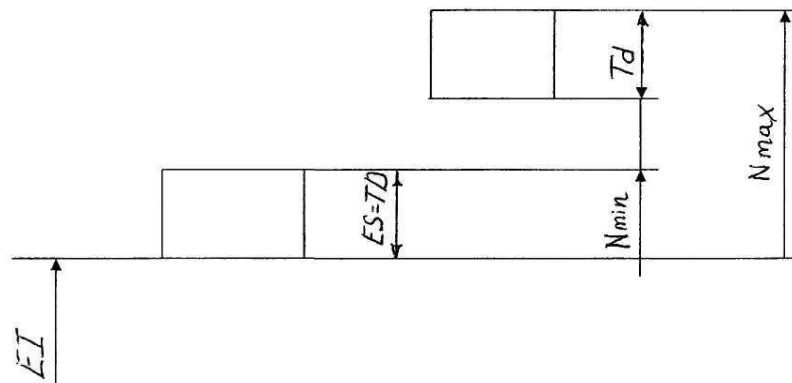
Схема расположения полей допусков деталей соединения.
